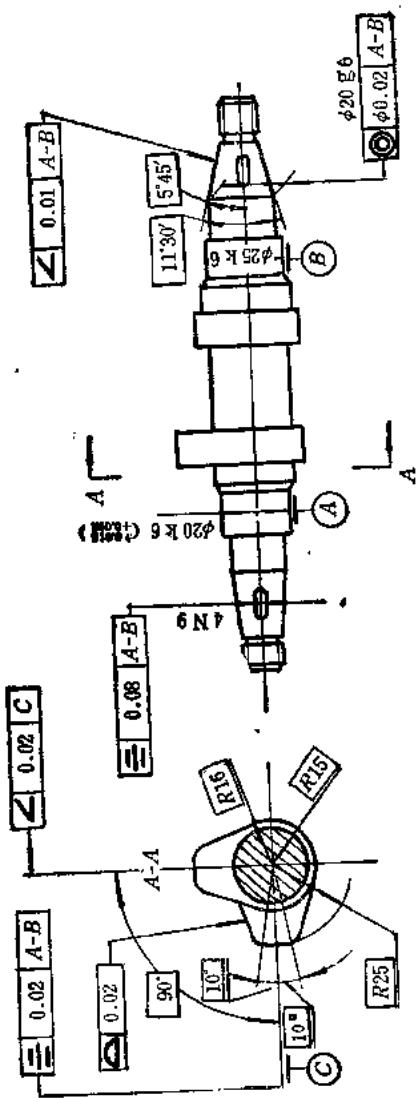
遵守独立原则的形位公差与尺寸公差的标注方法
